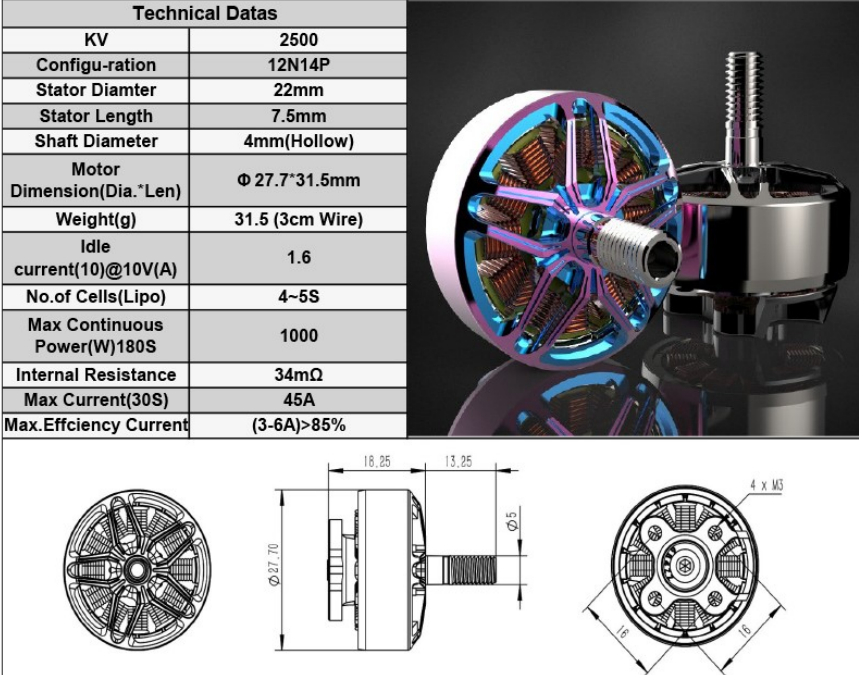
Zvolený motor RCINPower GTS v2 2500kv [18]
